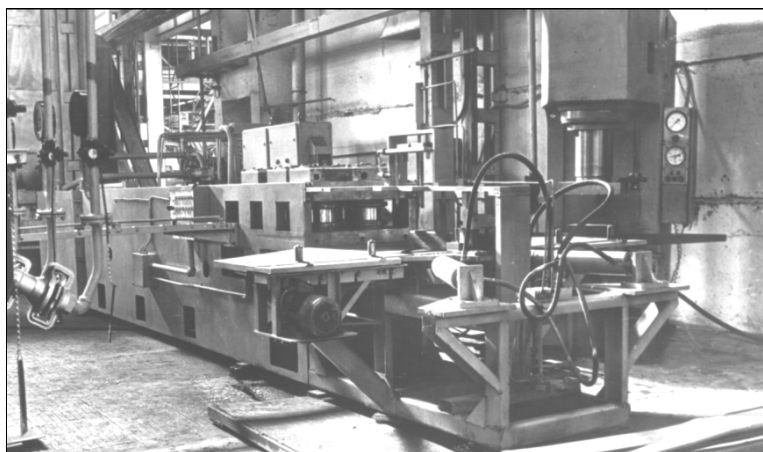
Модернизированный прокатный стан для прокатки заготовок направляющих элементов пневмоподвески
